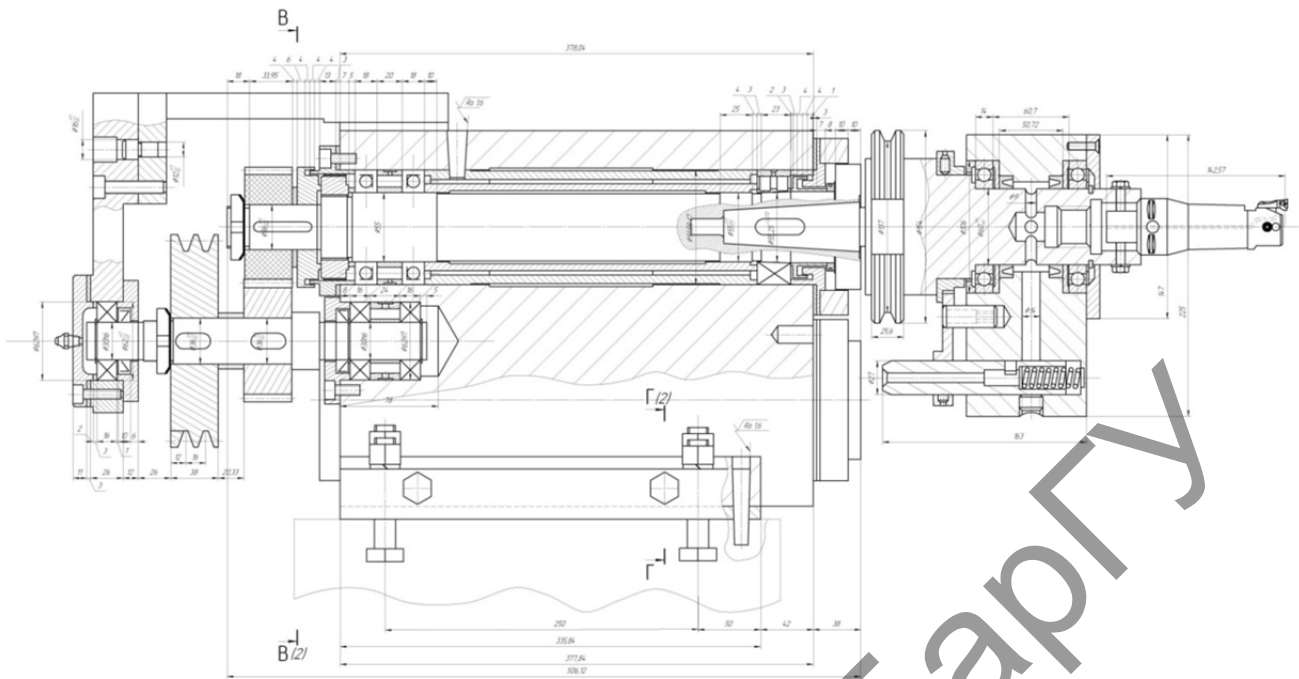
Сборочная схема шпинделя расточного станка с патроном для подвода СОТС и расточной оправкой
